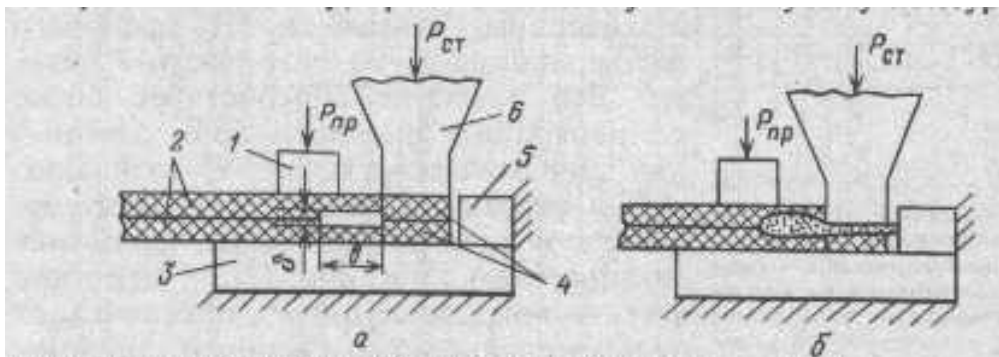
Схема ультразвуковой сварки вытесненным расплавом а - начало сварки; б - ее окончание; 1 – прижим; 2 – свариваемые детали; 3 – опора; 4 – технологические детали, подвергающиеся ультразвуковому воздействию; 5 – упор; 6 – волновод;  $P_{пр}$  – давление прижатия;  $P_{ст}$  – статическое сварное давление;  $\delta$  и  $\epsilon$  – толщина и ширина технологического зазора соответственно
